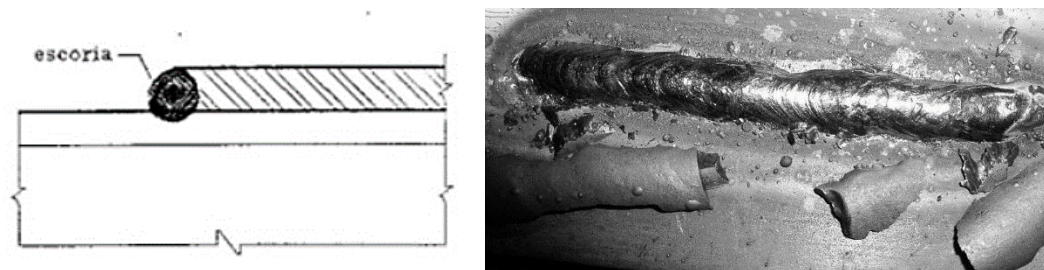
Detalle de falla en conexión soldada por ilusión de escoria
